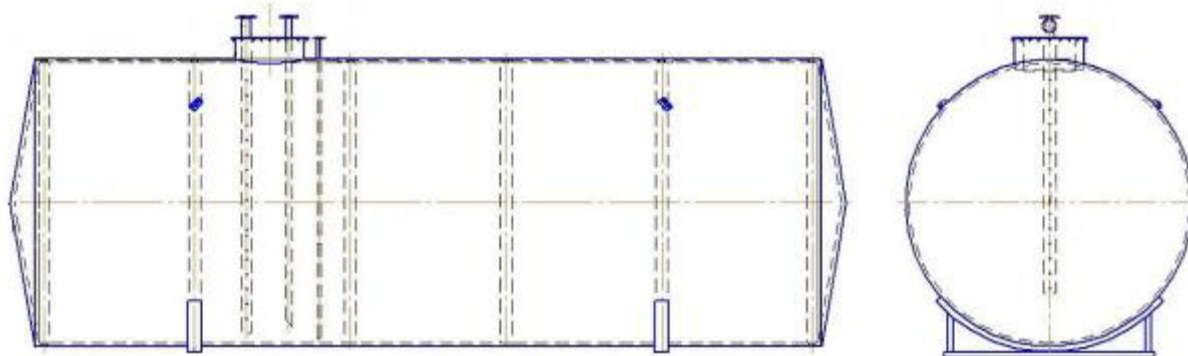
Эскиз общего вида резервуаров РГС-25 зав.№№ 1, 2, 3
